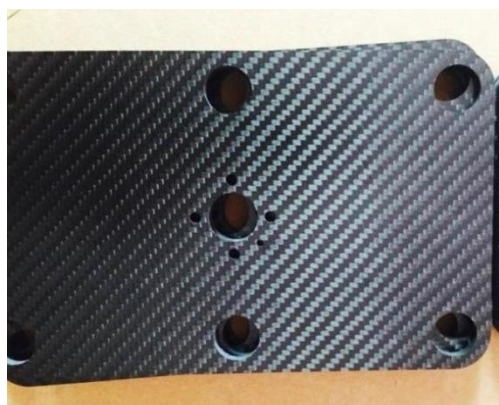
Типичные изделия из углепластика с механически образованными поверхностями
